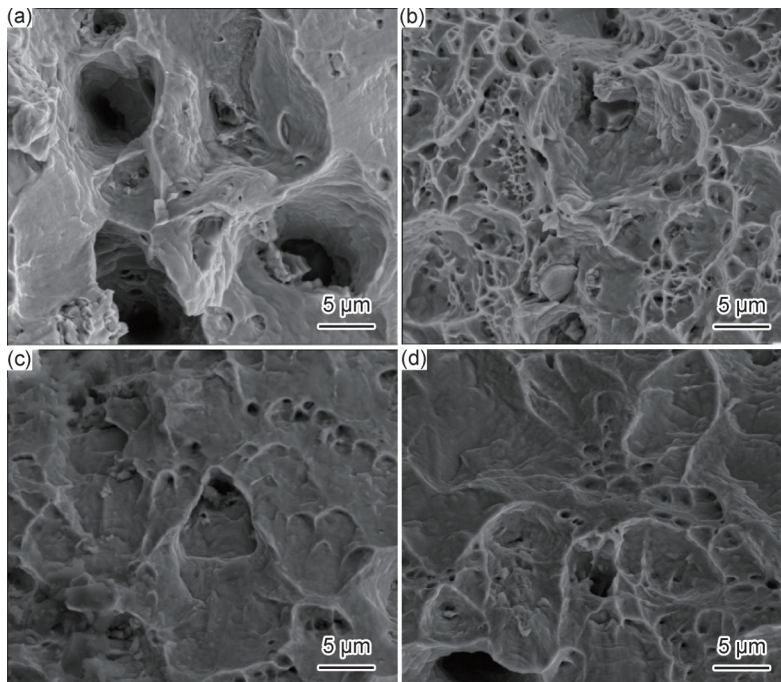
不同工艺制备的两种规格 GH3625 合金管材 600 °C 高温拉伸断口形貌
